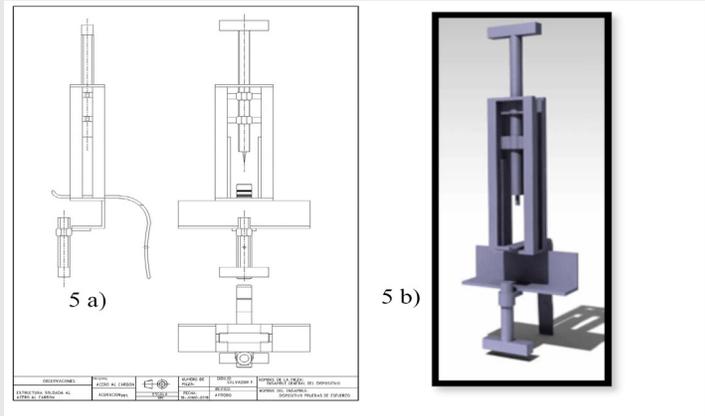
Diseño de dispositivo de prueba de esfuerzo
